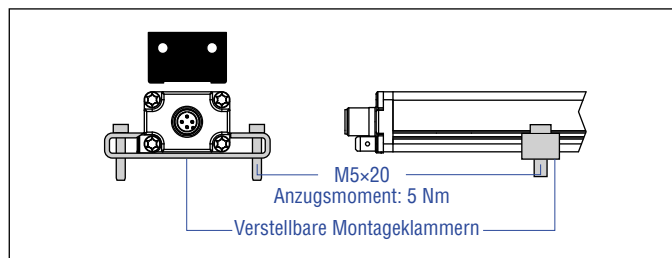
Montageklammern mit Zylinderschraube M5×20 (Artikelnr. 403 508)
